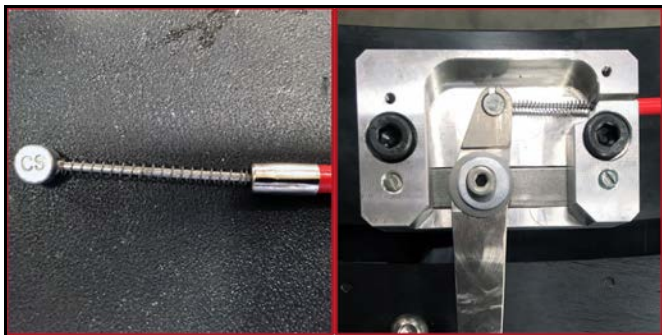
EXTREMO DEL CABLE CON MUELLE, CASQUILLO INSTALADO EN LA CARCASA DEL CABLE (IZQUIERDA); CABLE INSTALADO EN LA CARCASA DEL ACTUADOR (DERECHA)
